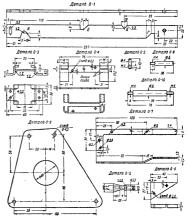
Паразитный ролик рабочего хода (узел 6) и перемотки (узел 6А) и его детали; 6-1— корпус ролика (дюралюминий Д16Т)— 1 шт.; 6-2 подвижная площадка (сталь 20) — 1 шт.; 6-3 — уголок (сталь 20) — 1 шт.; 6-4 — направляющий стержень (сталь 45) — 1 шт.; 6-5 — скоба (сталь 20) — 1 шт.; для узла  $6 \, l = 32$  мм и для узла  $6A \, l = 65$  мм;  $6 \cdot 6 -$  кольцо стопорное (сталь 25) — 1 шт.; 6-7 — стержень (сталь 45) — 1 шт.; 6-8 ось паразитного ролика (сталь У8А)— 1 шт.; 6-9 — кольцо резиновое —1 шт.; 6-10-кольцо (дюралюминий Д16Т)-1 шт.; 6-11 — вилка (сталь 20) — 1 шт.; 6-12 — упор (сталь 45) шт.; 6-13 — прижина диаметром 6,5 мм и длиной 45 мм (28 виткав проволоки марки Н диаметром 6-14 — винт мм) — I шт.; M3 × 6 мм (сталь 3) — 8 шт.; 6-15 шайба (сталь 3)— 1 шт. Указанные количества деталей относятся к одному узлу (6 или 6А)
